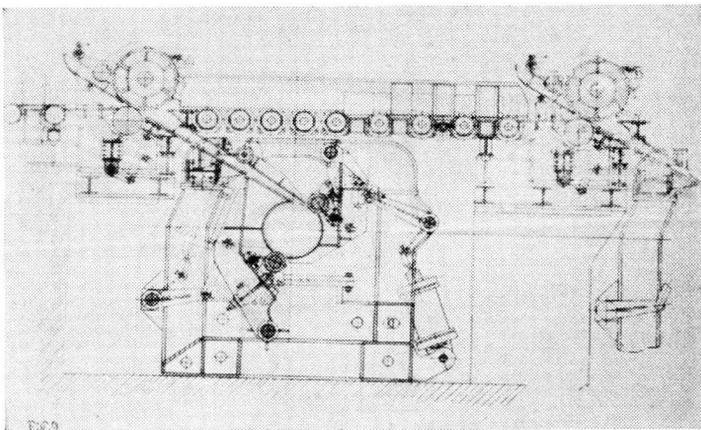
Secção longitudinal de uma bobinadora, com apenas dois rolos enroladores.
